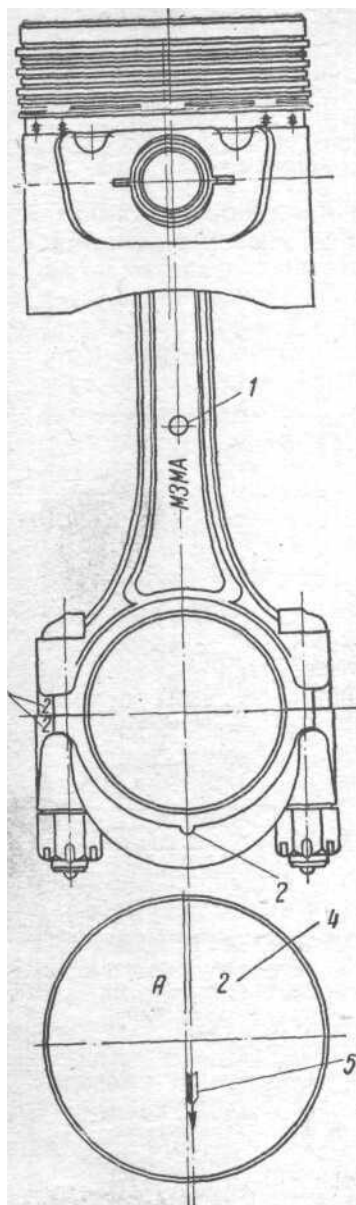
Установочные выступы и метки на поршне, шатуне и крышке шатуна:
